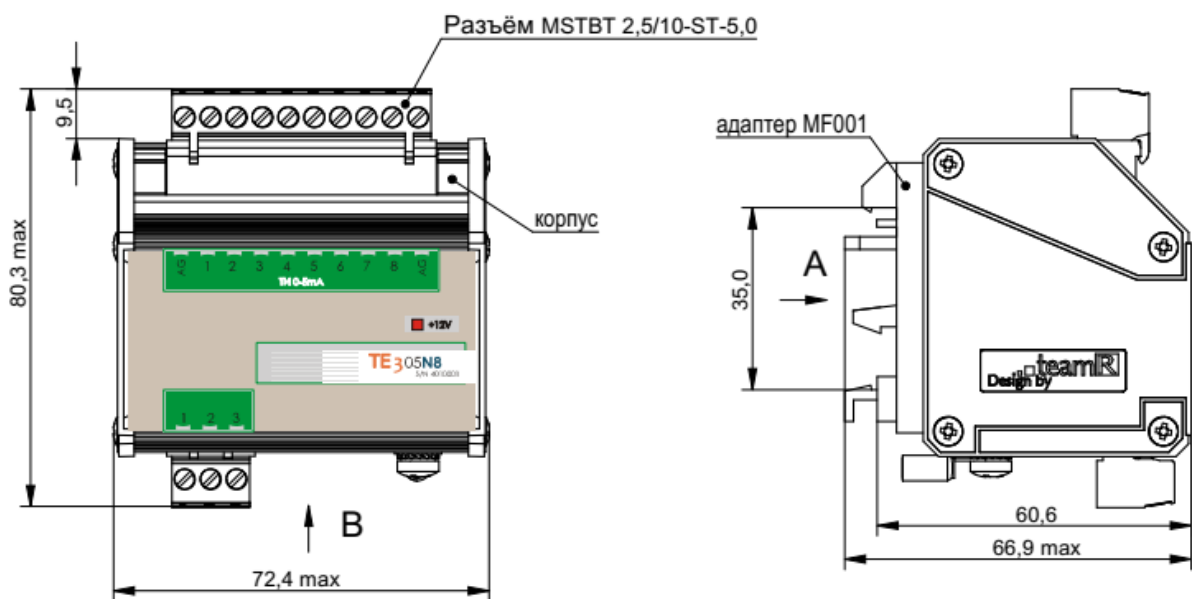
Габаритный чертеж блока «ТЕ305N8»
